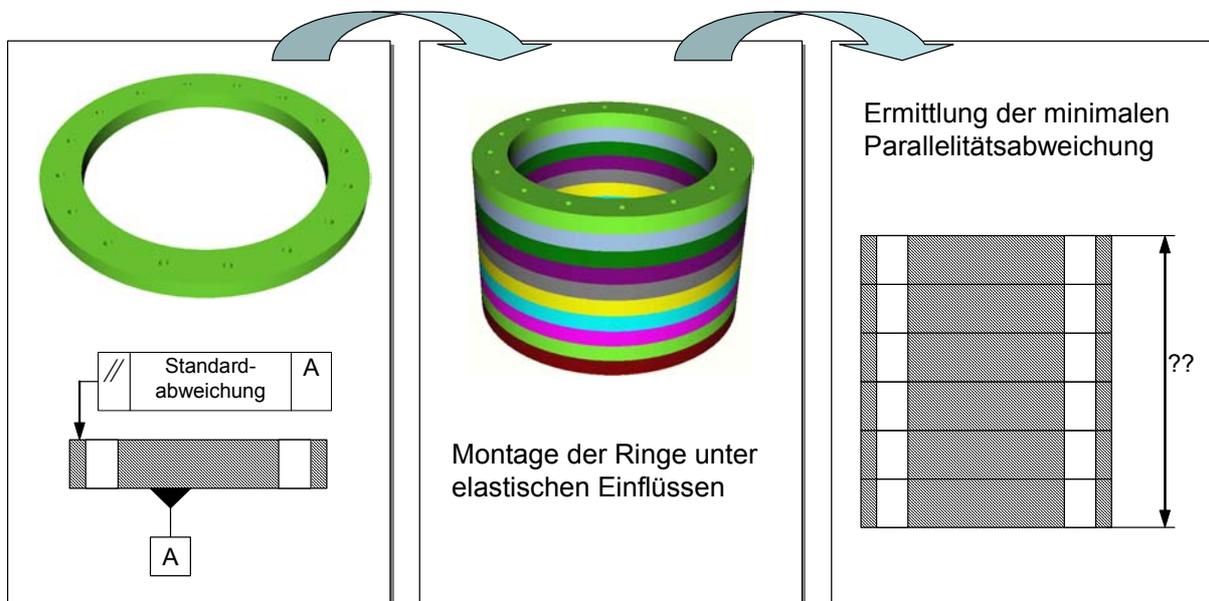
Kreisringförmiger Demonstrator mit dazugehöriger Tolerierung
